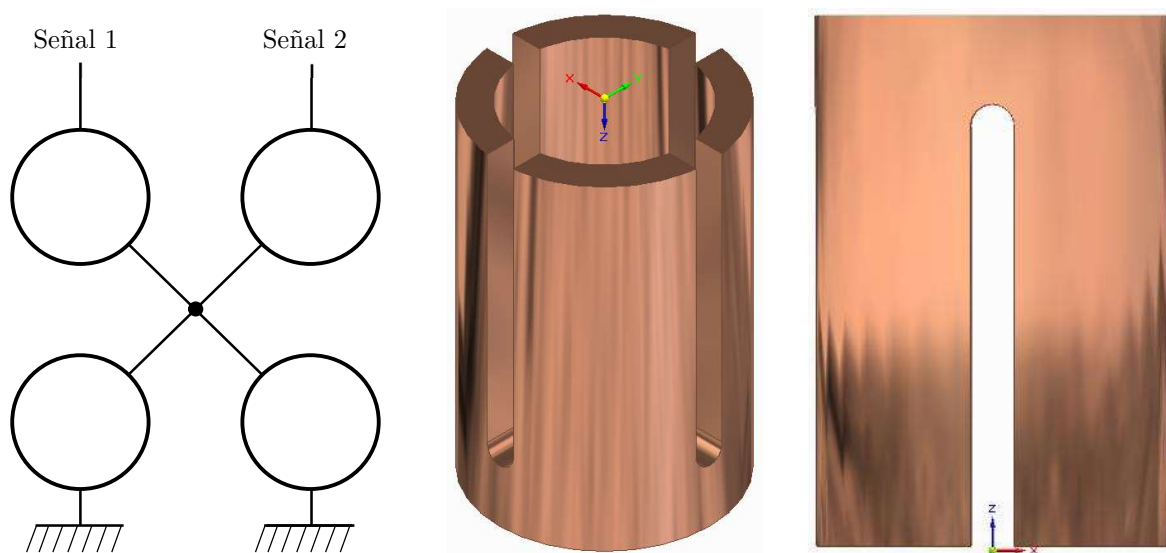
Esquema eléctrico del estátor del microactuador 1Fr (izquierda) y vistas del CAD del estátor (derecha).
